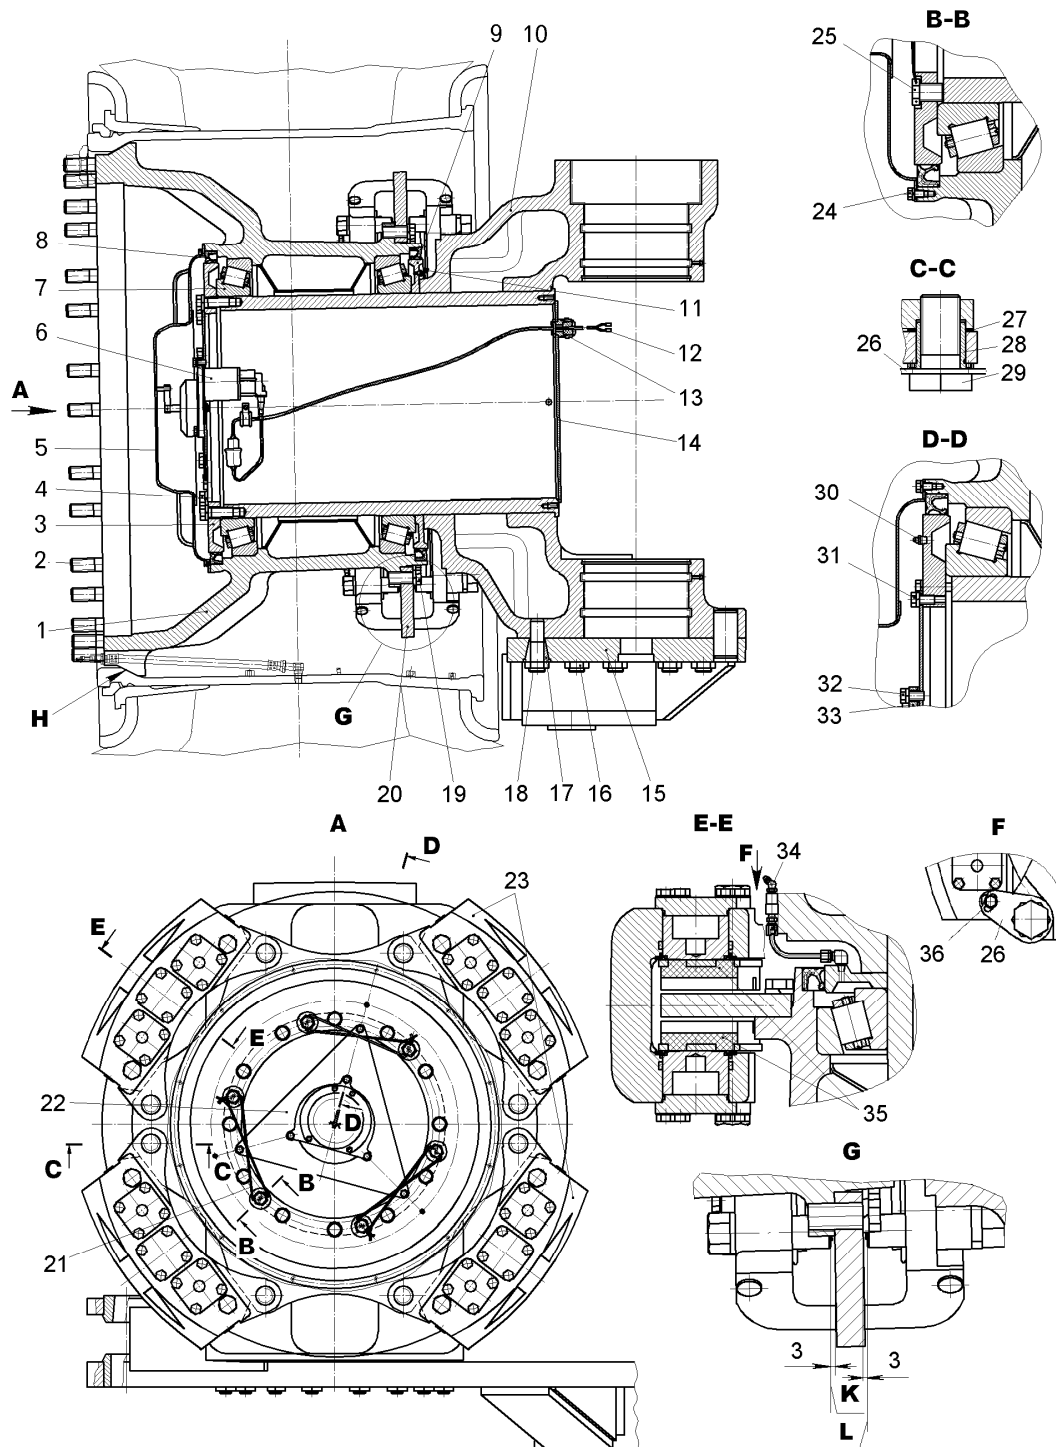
Кулак поворотный со ступицей и тормозами:
